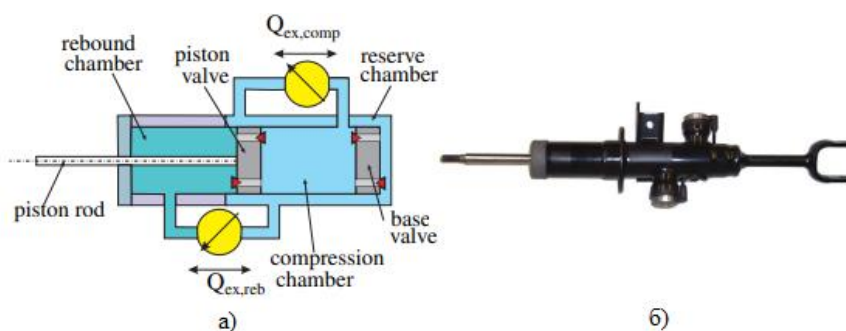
Адаптивный амортизатор с двумя клапанами: а) – схема внутреннего устройства амортизатора; б) – его внешний вид
